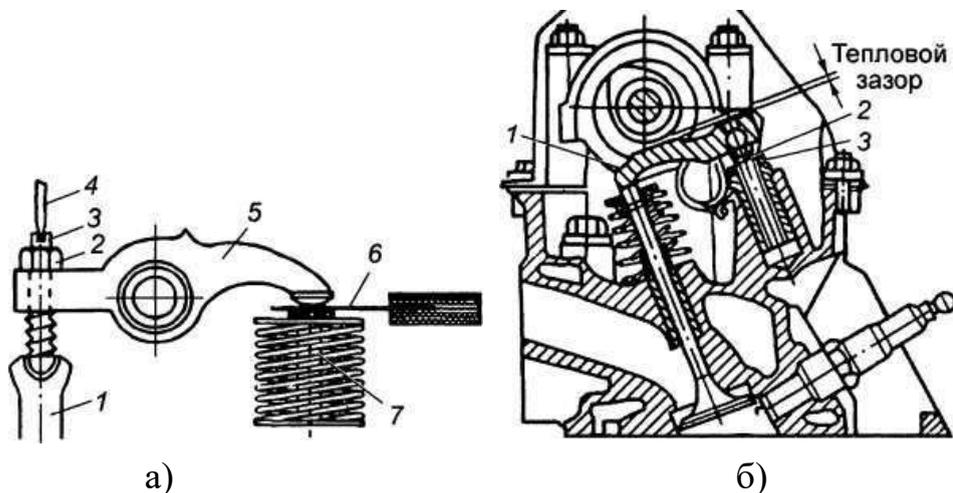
Проверка и регулировка теплового зазора ГРМ:
